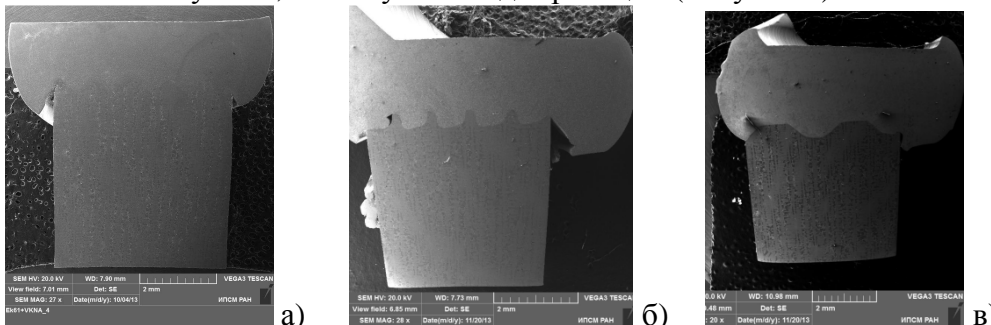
Общий вид соединенных образцов с различным рельефом поверхности соединения
